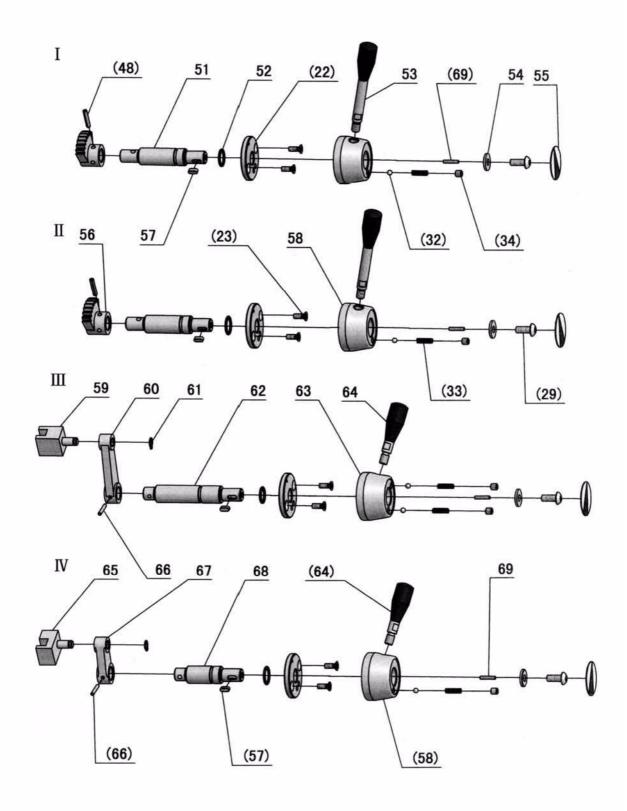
Spindelstock 2 von 8 - Headstock 2 of 8
